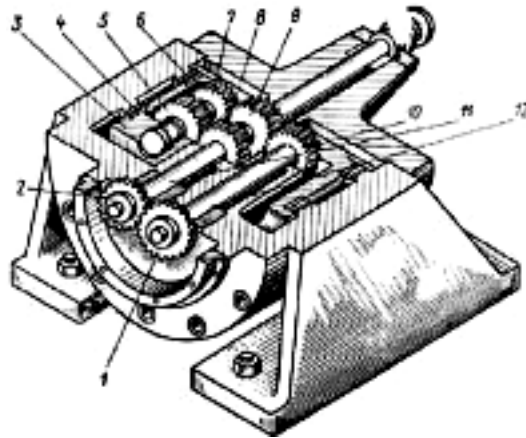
Стенд с перемещаемыми в окружном направлении отдельными зубчатыми колесами
